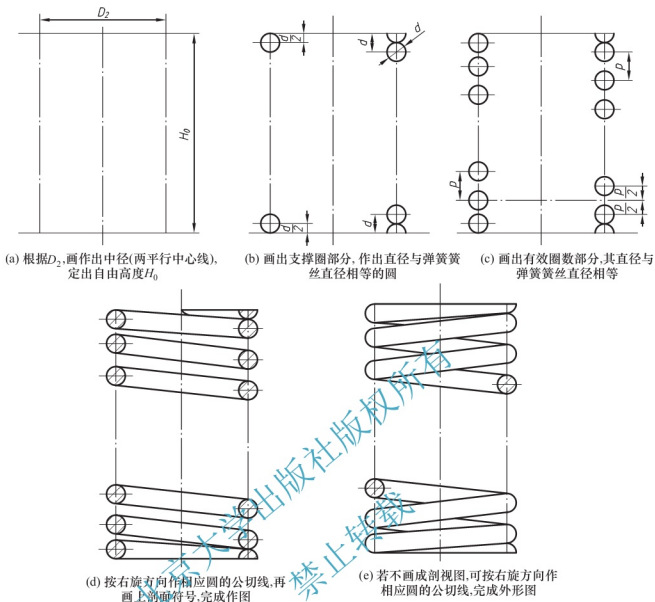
圆柱螺旋压缩弹簧的画图步骤
